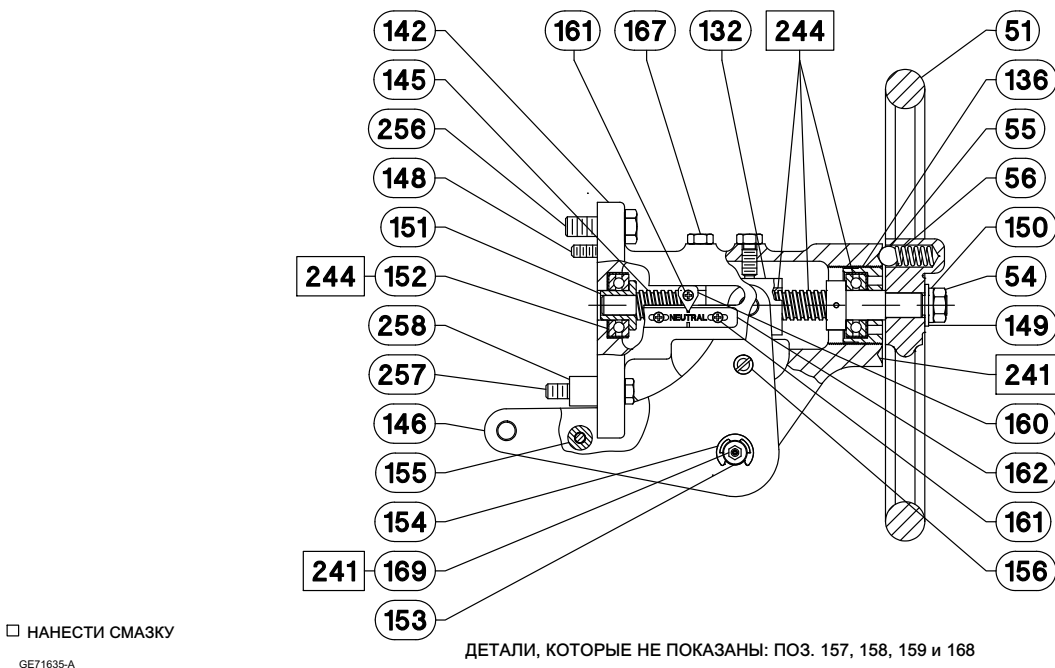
Боковой ручной дублер для приводов размером 45 - 60
